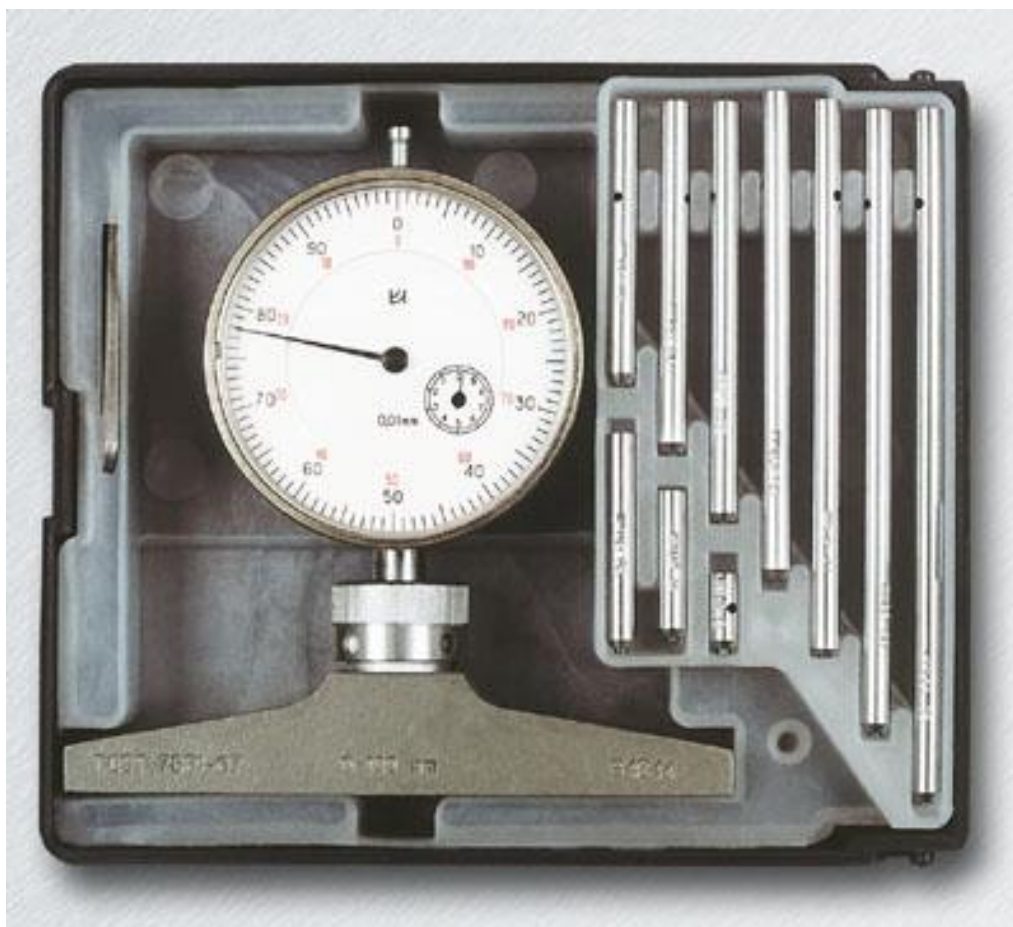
Общий вид глубиномера индикаторного ГИ-100
